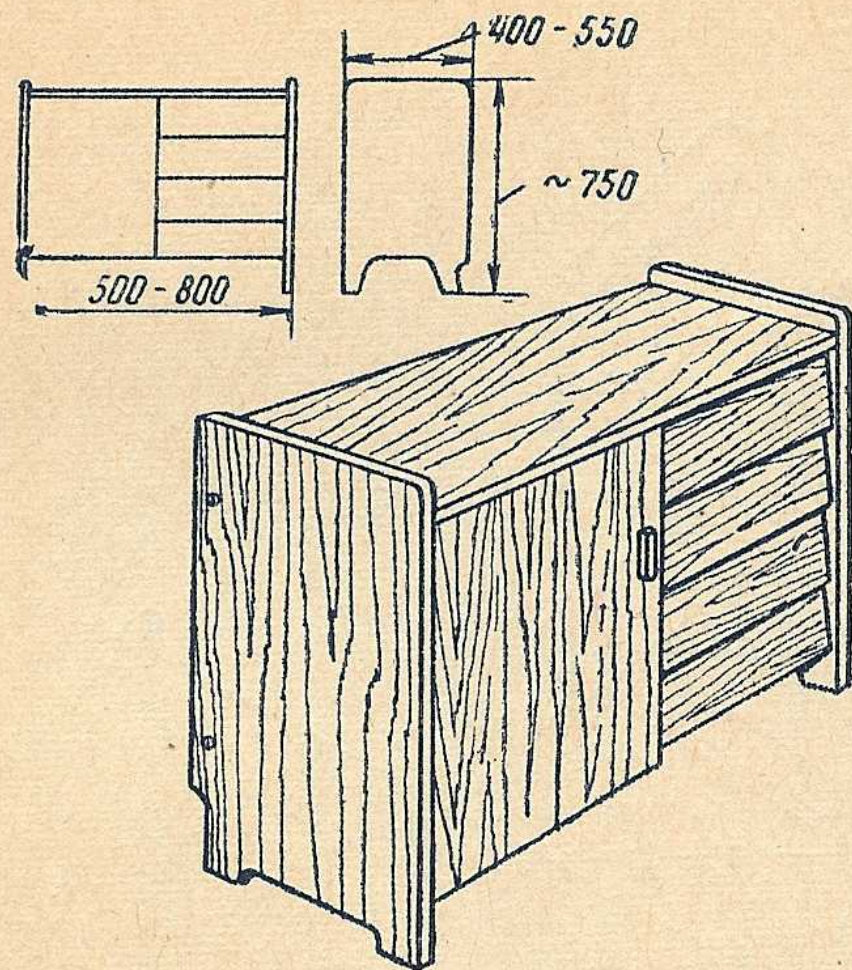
Тумбочка под телевизор (внешний вид и конструкция)
